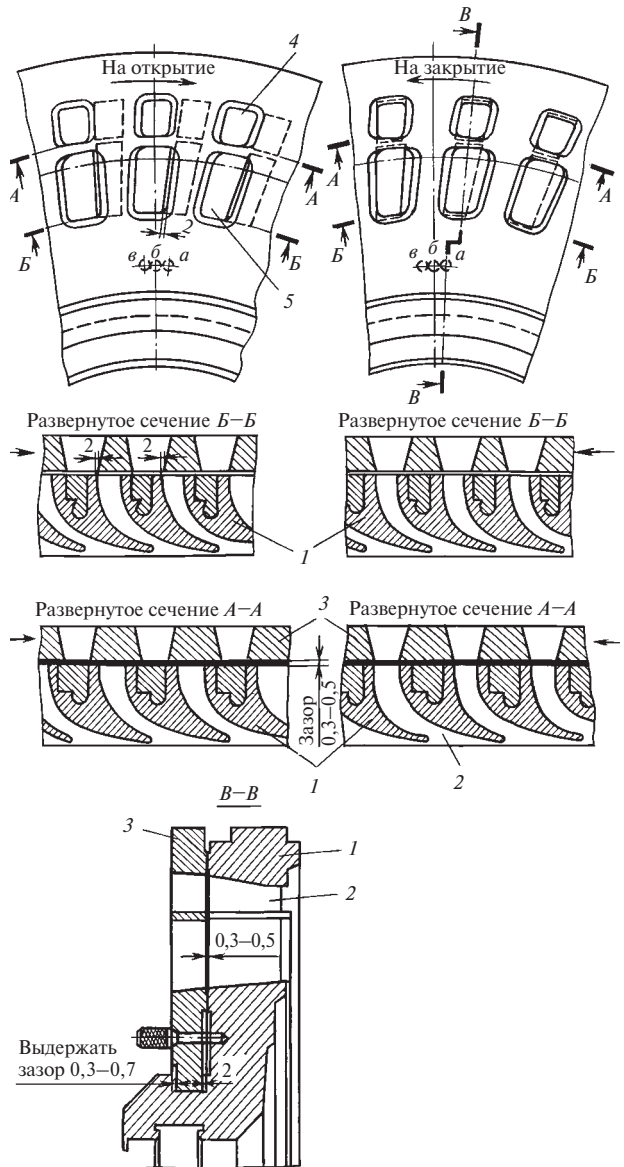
Поворотная диафрагма конструкции ЛМЗ
